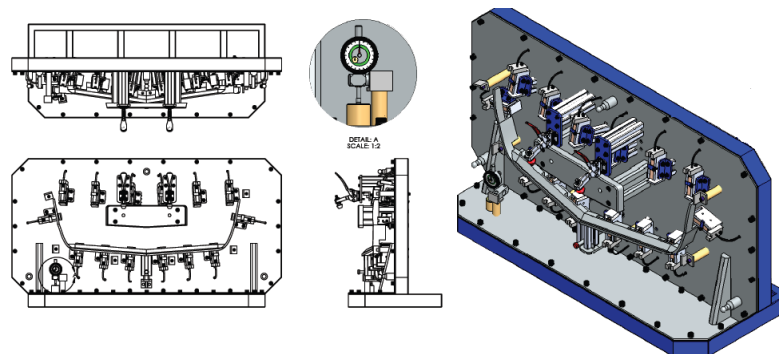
Vistas del diseño y ensamble del Cheking Fixture en Solidworks 2017.
